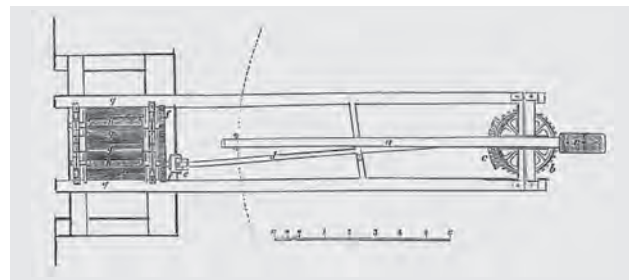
Grundriß eines mit Pferden über Göpel betriebenen Walzwerks
